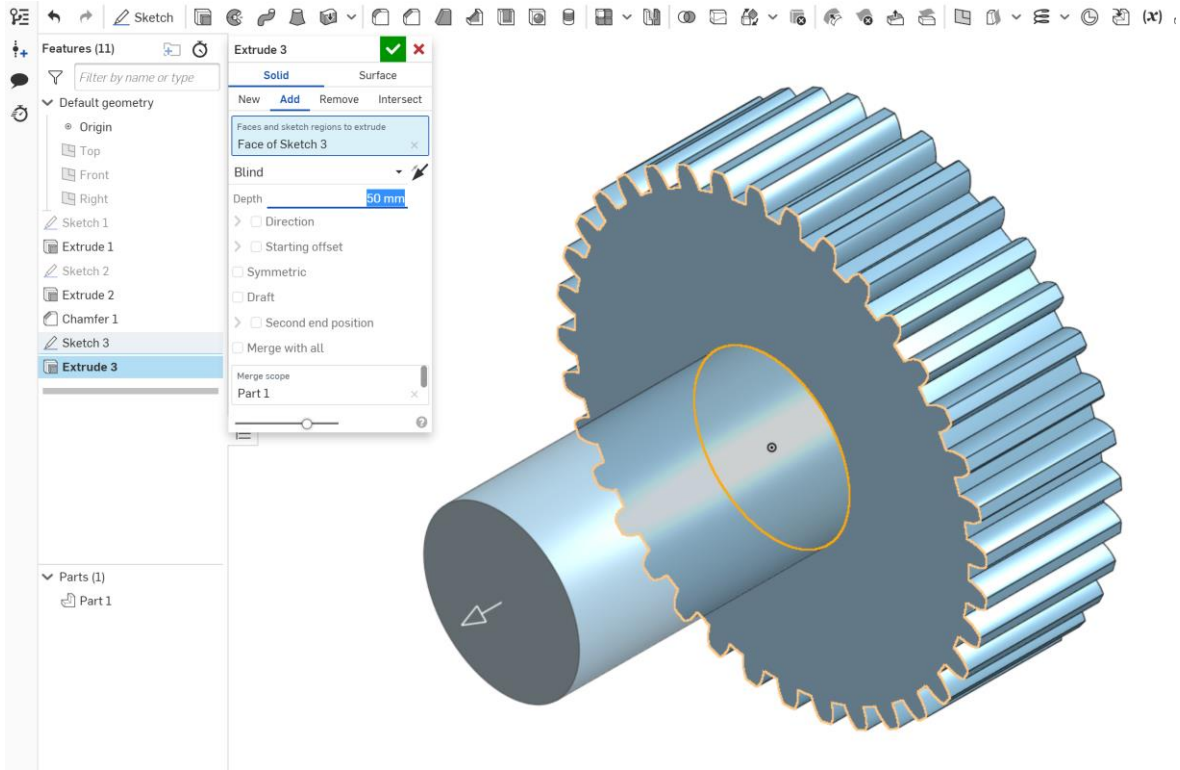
Використовуючи операцію Extrude, формуємо вал.
